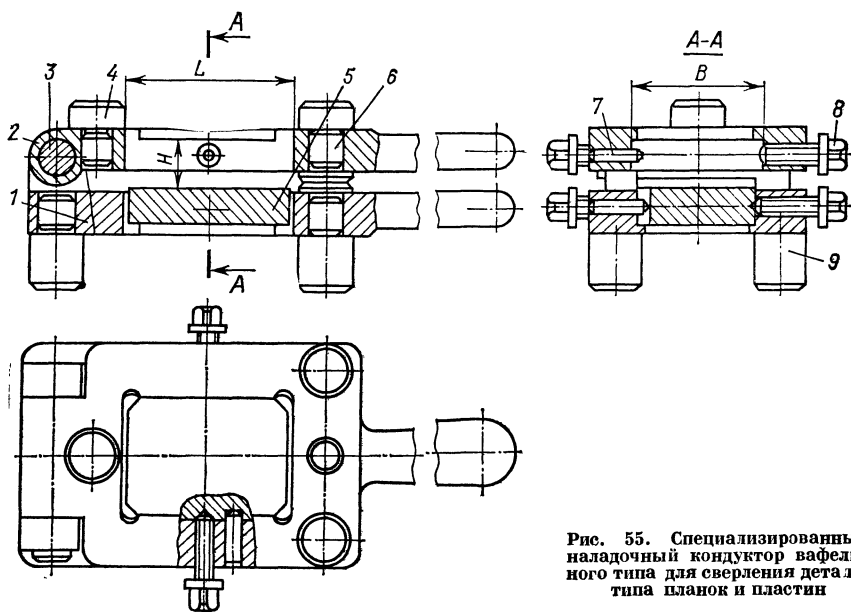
Специализированный наладочный кондуктор вафельного типа для сверления деталей типа планок и пластин
